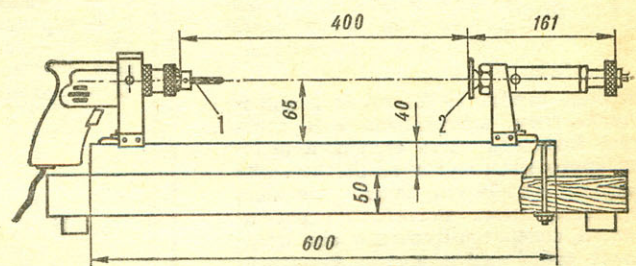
Сверлильный станок: 1 — сверло, 2 — грибок.
